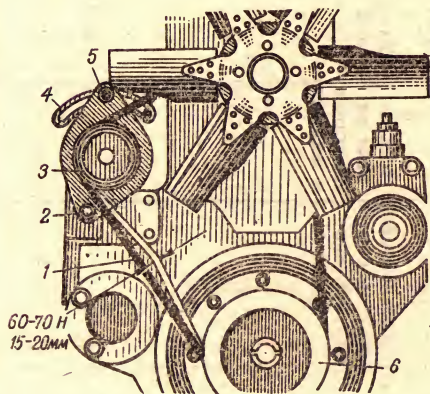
Устройство для натяжения ремня привода вентилятора и генератора двигателя СМД-14:
